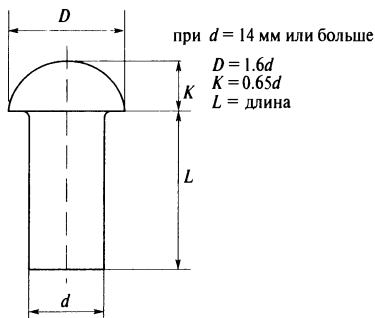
Полукруглая головка заклепки, изготовленная методом горячей штамповки
